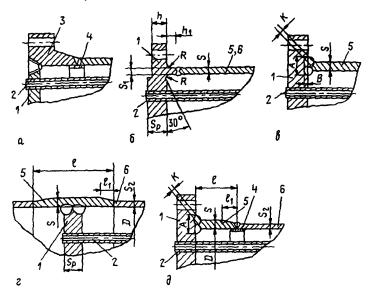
Конструкция сборочной единицы крепления трубной решетки аппаратов типов Н и К.
